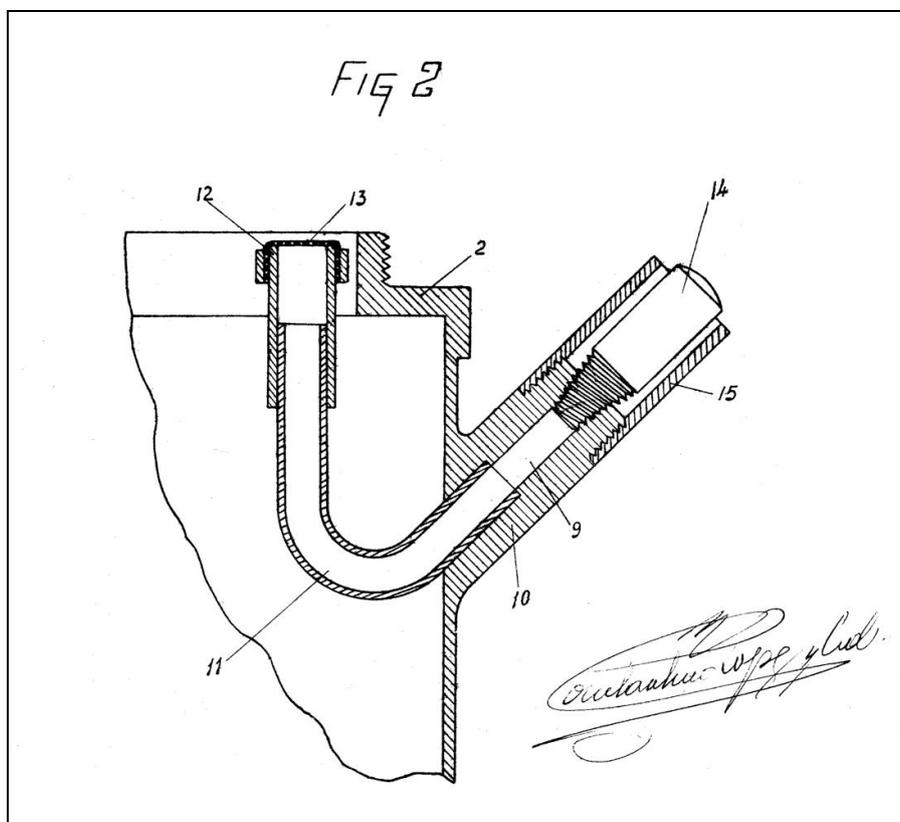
Detalle del perfeccionamiento patentado (Arch. J.M. Sanchis)
